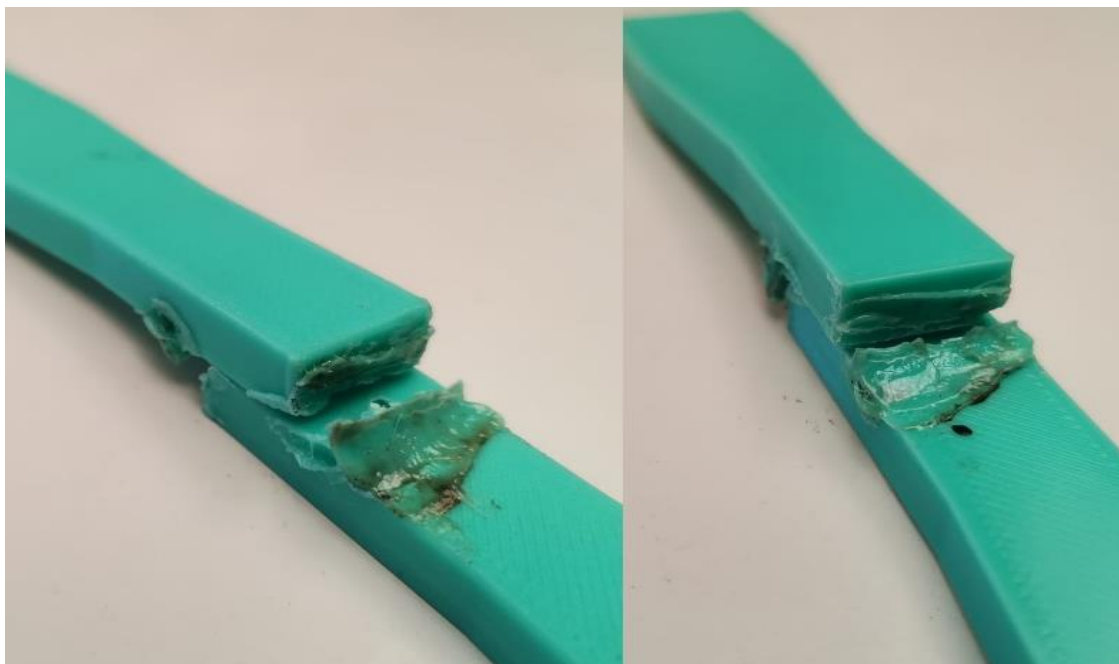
Fractura probeta PC3 - Unión en traslape con E.C.
